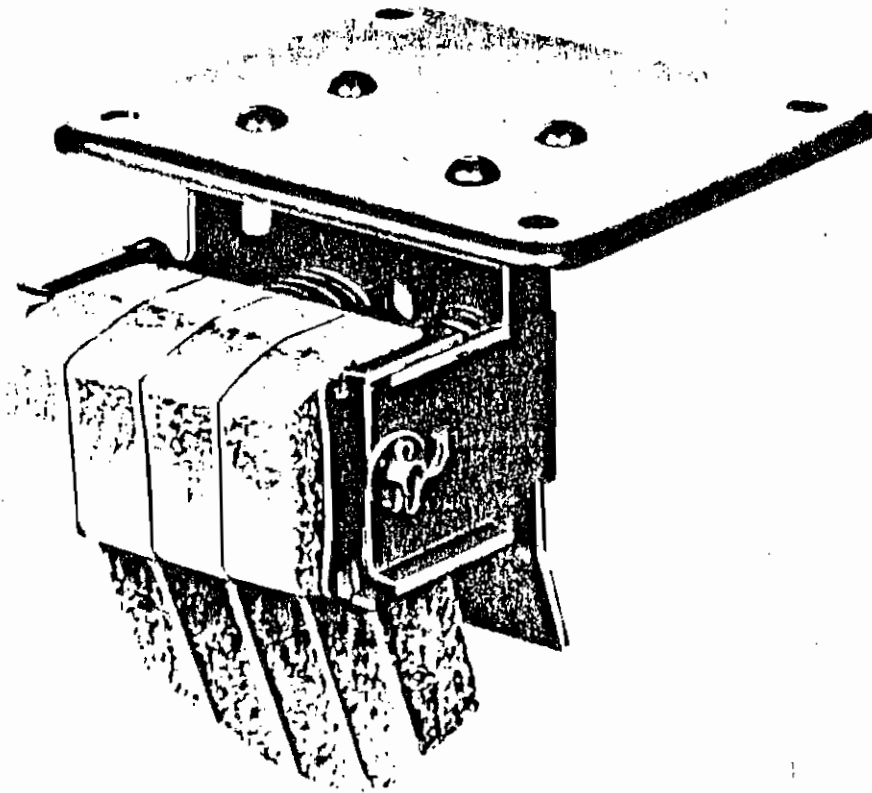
Juego de partes armadas para formar un lubricador de mecha
